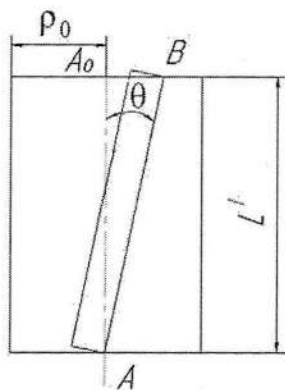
Заготовка в исходном положении (вид сверху)
